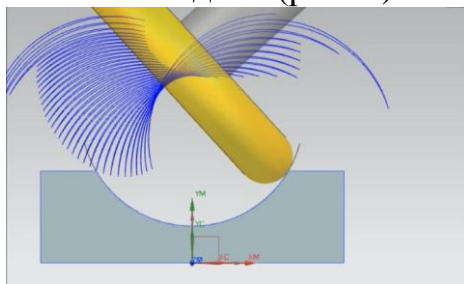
Модель траектории движения инструмента с возвратно-качательным движением подачи
